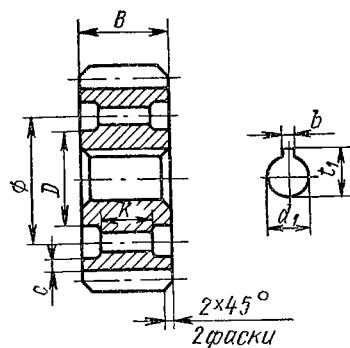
Конструктивные размеры цилиндрического зубчатого колеса:
